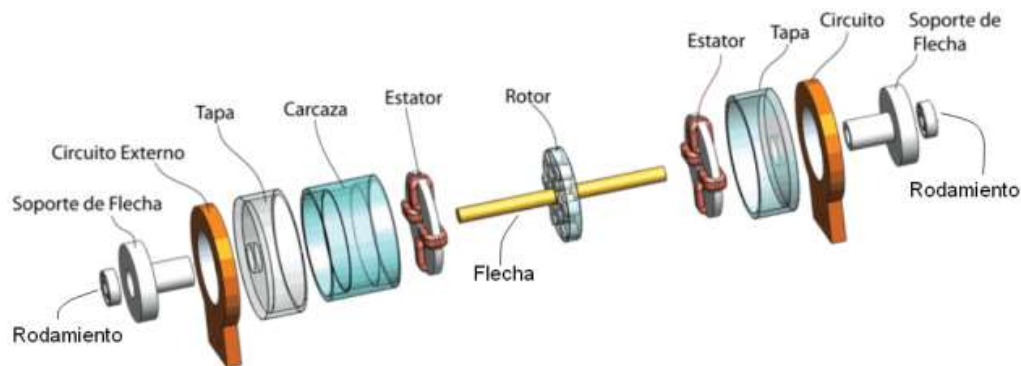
Explosivo del motor a pasos de fuerza de Lorentz.
